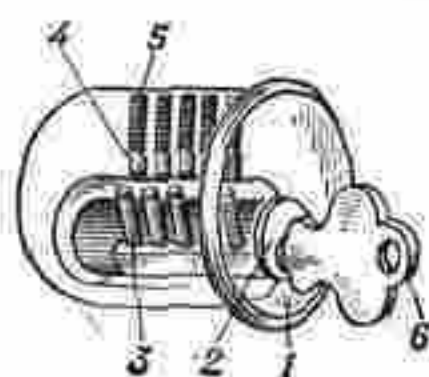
Цилиндрический механизм замка с ключом: 1 — корпус; 2 — сердечник; 3 — штифты сердечника; 4 — штифты корпуса; 5 — пружины; 6 — ключ.
